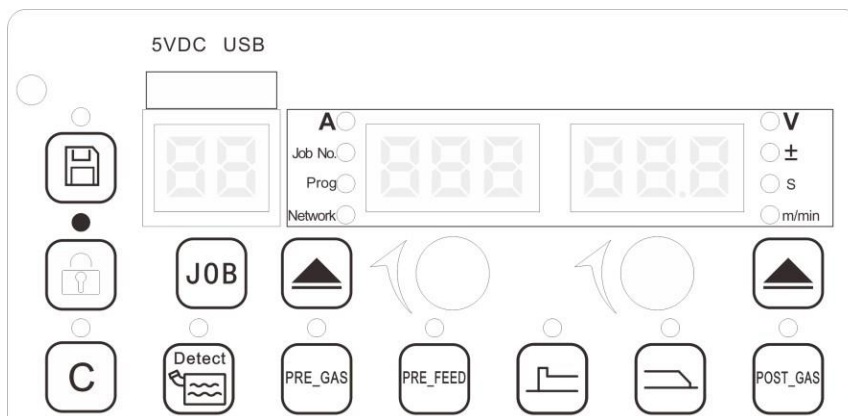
Блокировка панели управления сварочного источника питания
